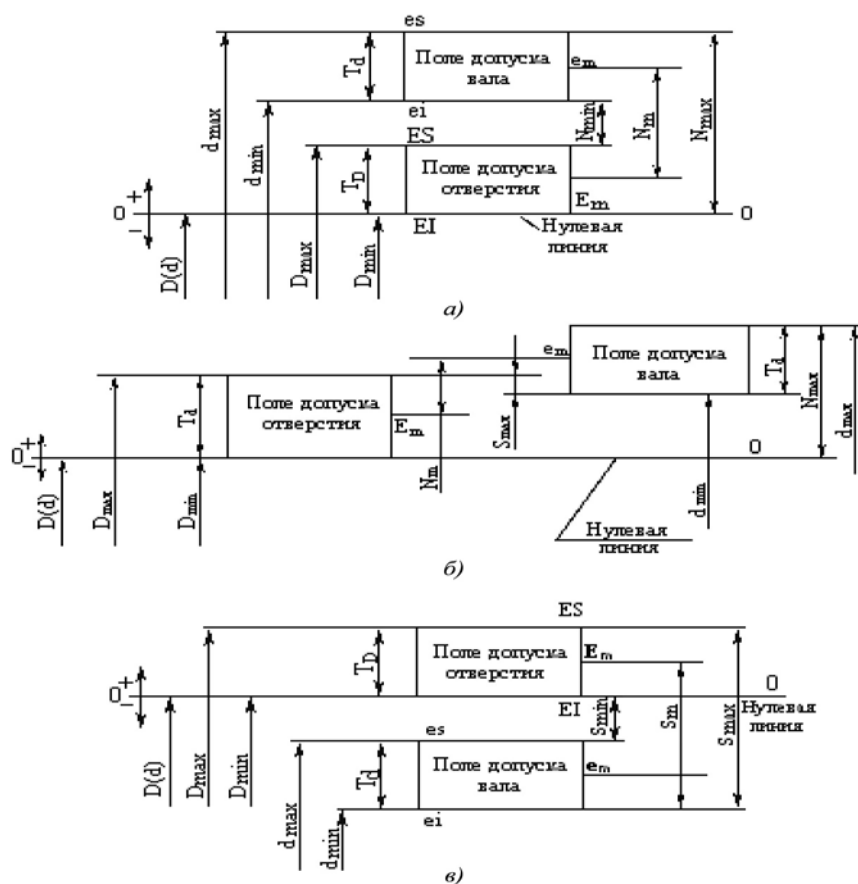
Сочетание полей допусков отверстия и вала для посадок: а - с натягом; б - переходных; в - с зазором
